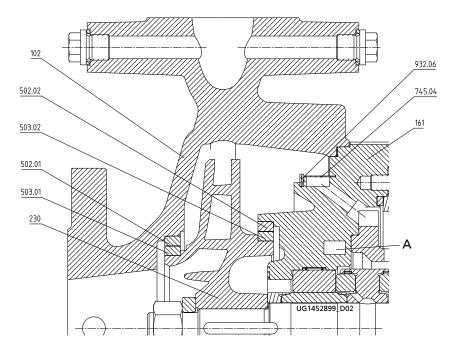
Исполнение спирального корпуса с кольцевым фильтром, камерой обогрева, щелевыми кольцами корпуса и рабочего колеса
